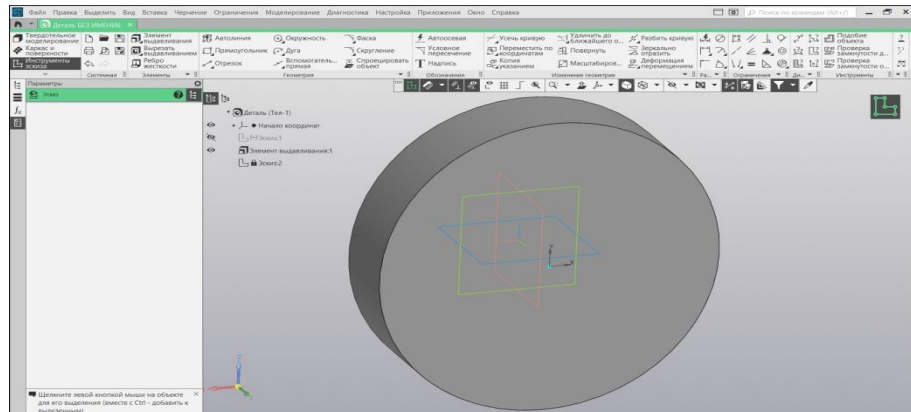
Цилиндрическая заготовка в среде Компас-3D
